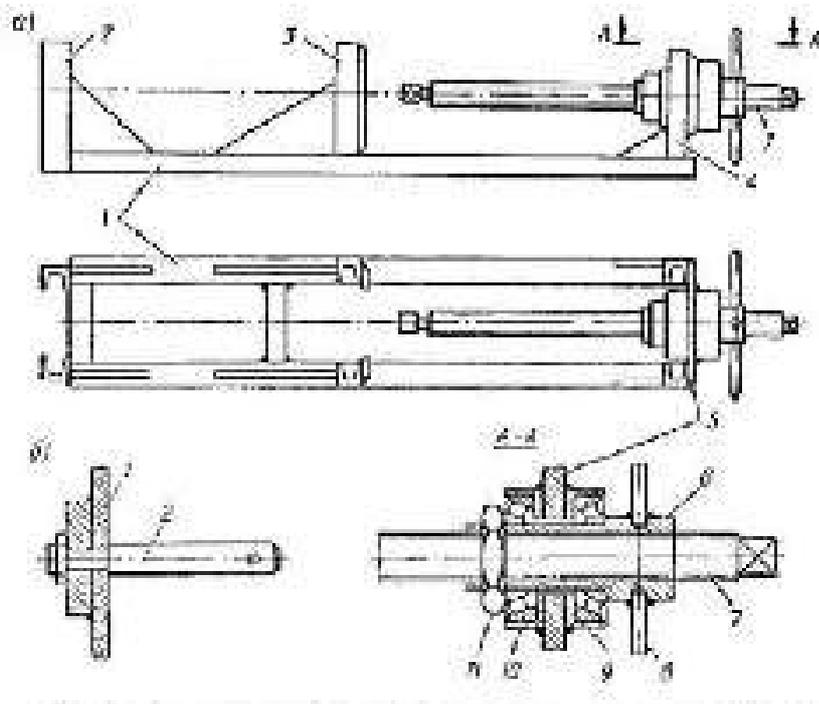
Стенд для разборки–сборки телескопического подъемника
